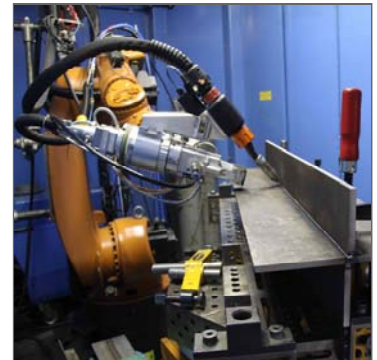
Laser-Hybrid-Schweißen einer Kehlnaht am Kreuzstoß
